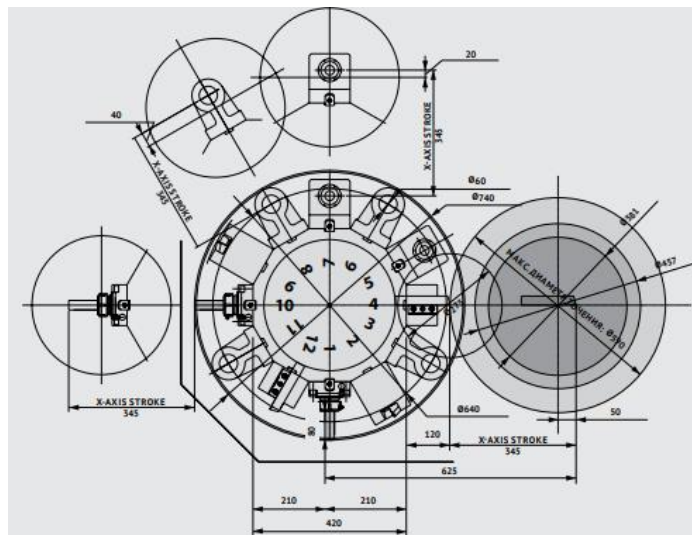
Револьверна головка токарно-фрезерного верстату
